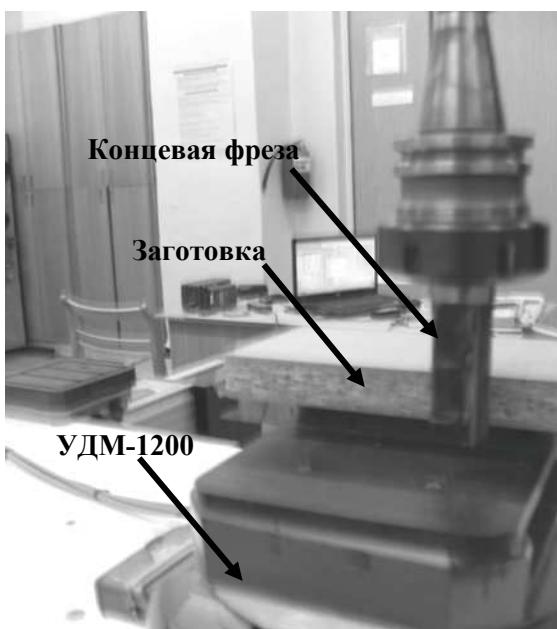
Заготовка, обрабатываемая в пределах базы УДМ-1200
